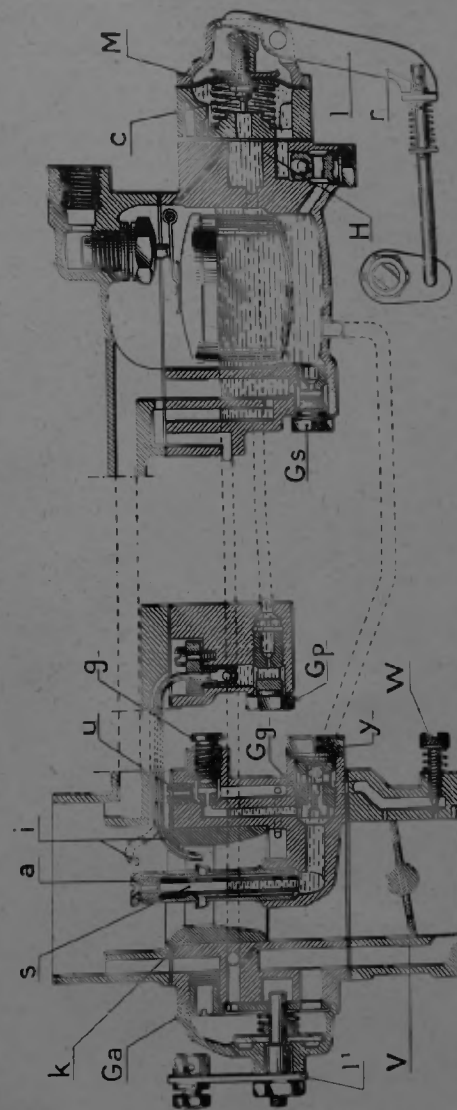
Coupe du carburateur inversé 32 PBL.
